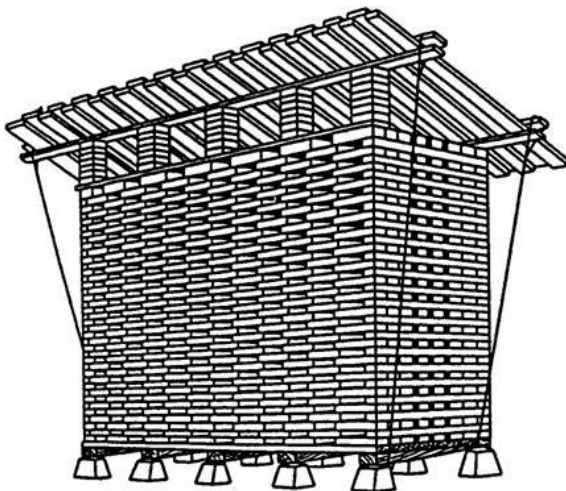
Штабель с разряженной укладкой пиломатериалов
